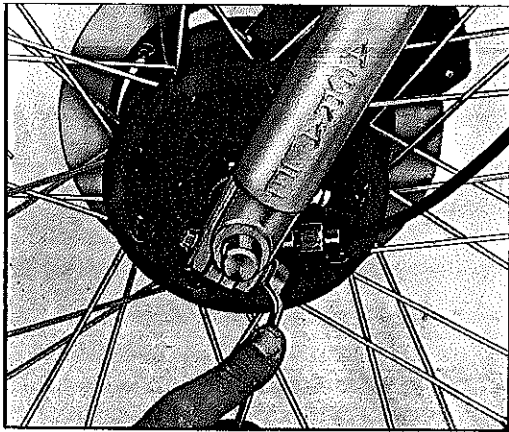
DESMONTAGEM DA RODA DIANTEIRA
